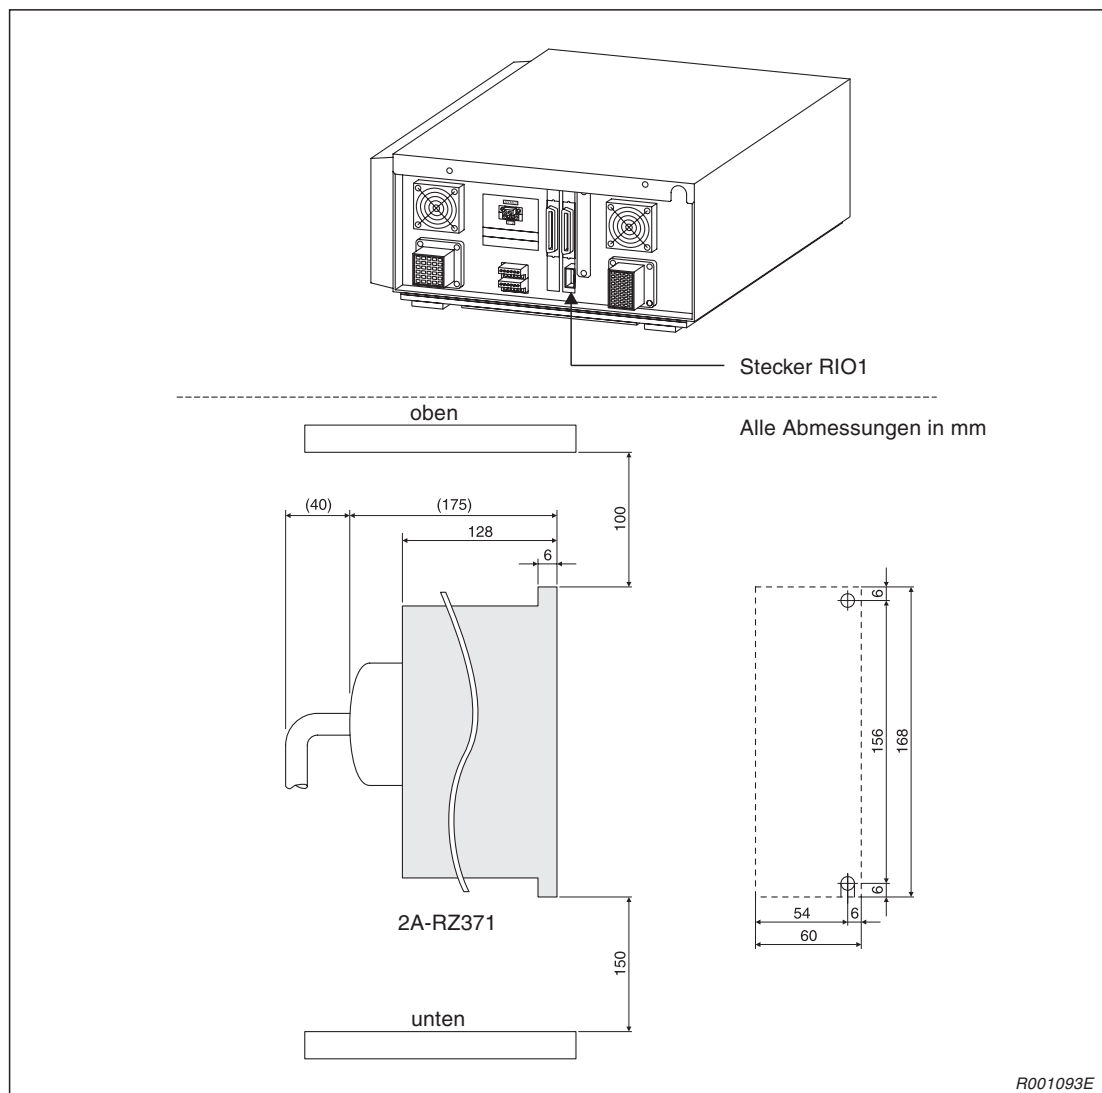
Installation der Ein-/Ausgangsschnittstelle
